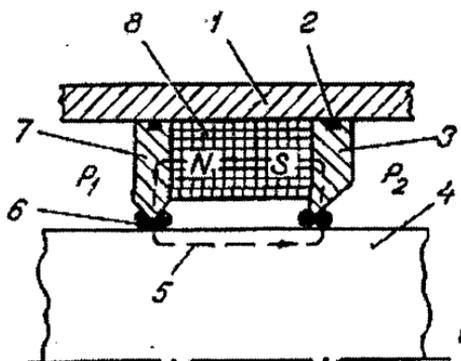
Принципиальная схема магнитожидкостного уплотнения и его рабочего зазора: 1- корпус; 2- уплотнительное кольцо; 3,7- полюса с асимметричным и симметричным профилем; 4- вал; 5- направление магнитного потока; 6- магнитная жидкость в уплотняемом рабочем зазоре; 8- магнит [5]
